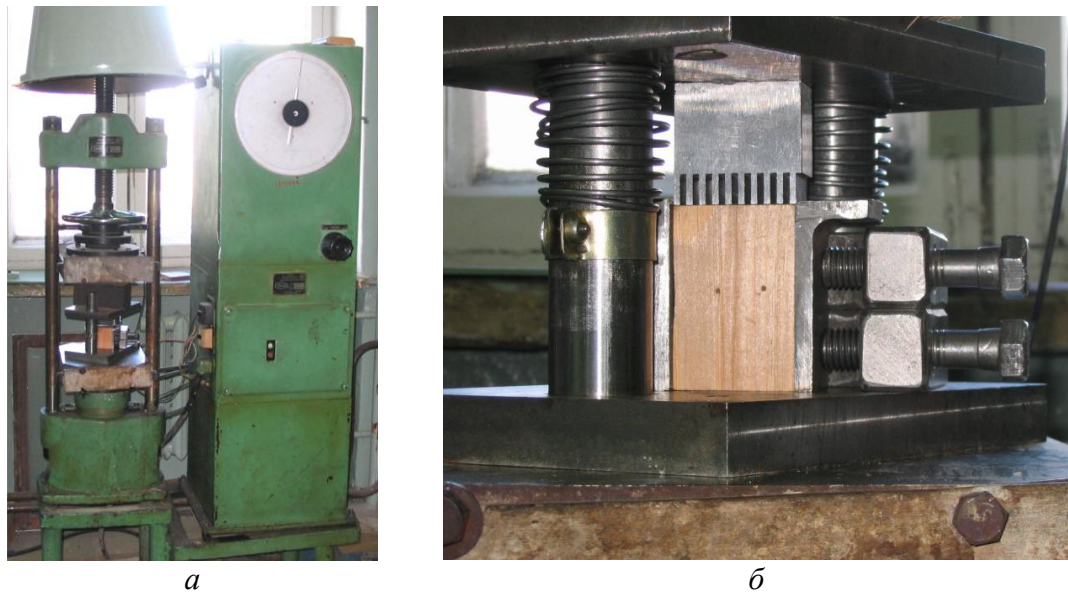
Лабораторная установка: *а* – общий вид пресса П-10 с оснасткой; *б* – оснастка для базирования, фиксации и обжима заготовок
